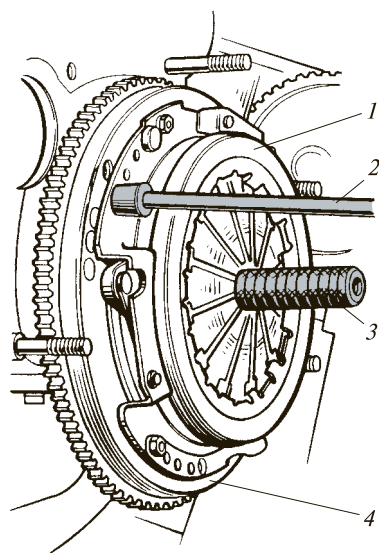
Установка нажимного диска сцепления с кожухом в сборе на маховик двигателя:
